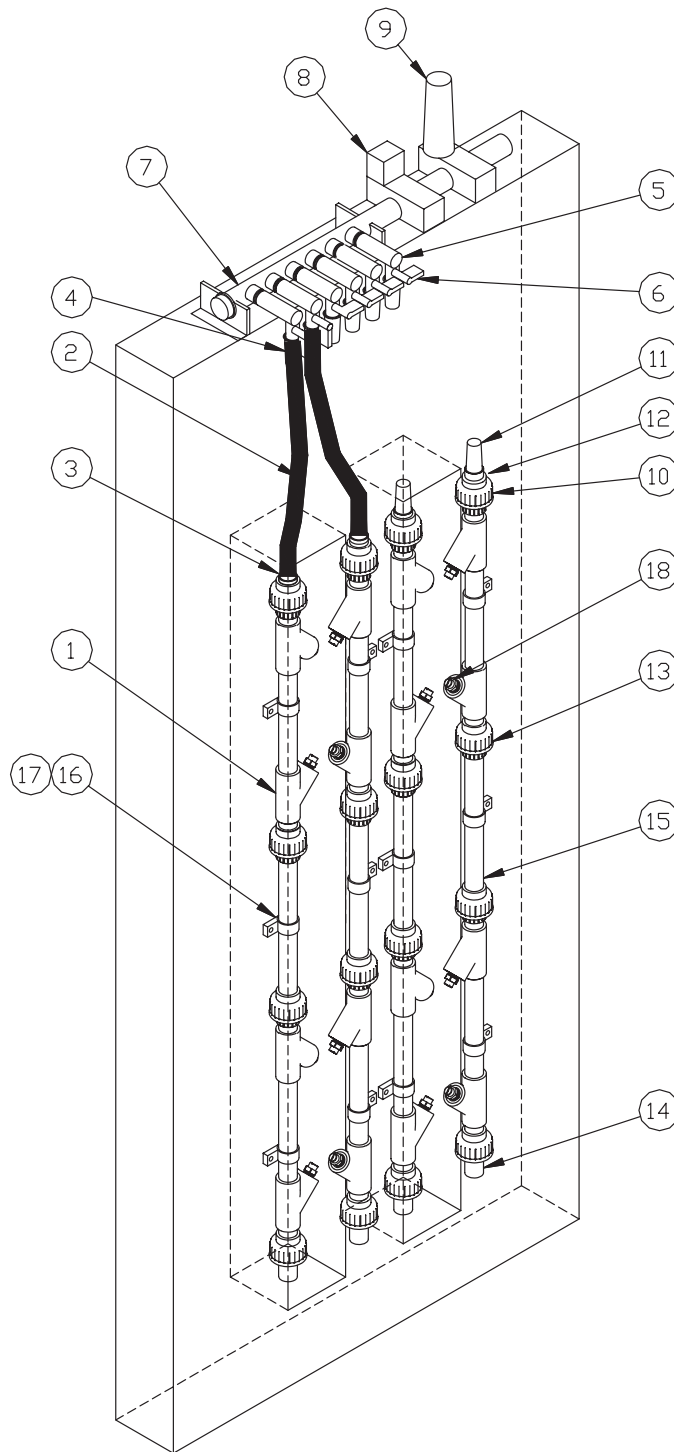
Dispositif de nettoyage extérieur du pistolet
